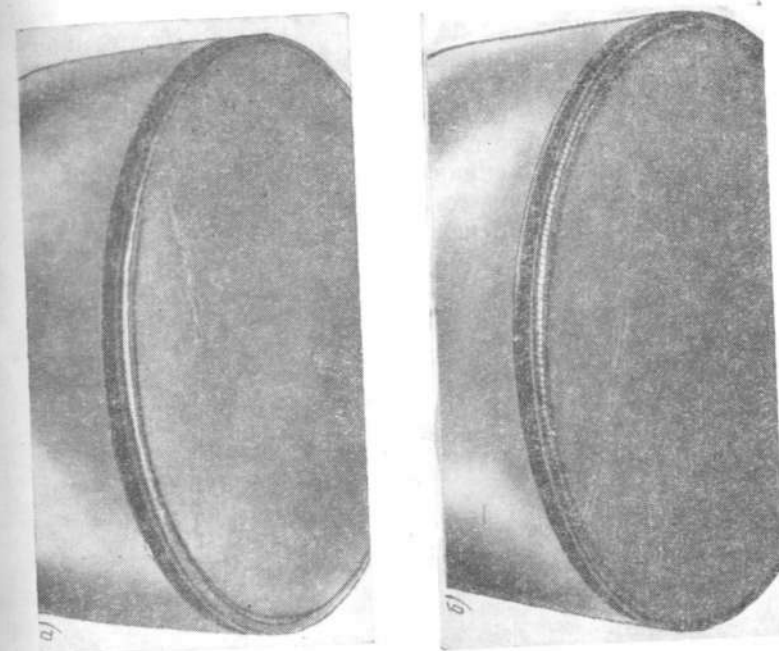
Внешний вид швов на соединении мембраны с корпусом: *а* — обычная сварка; *б* — импульсная сварка.
